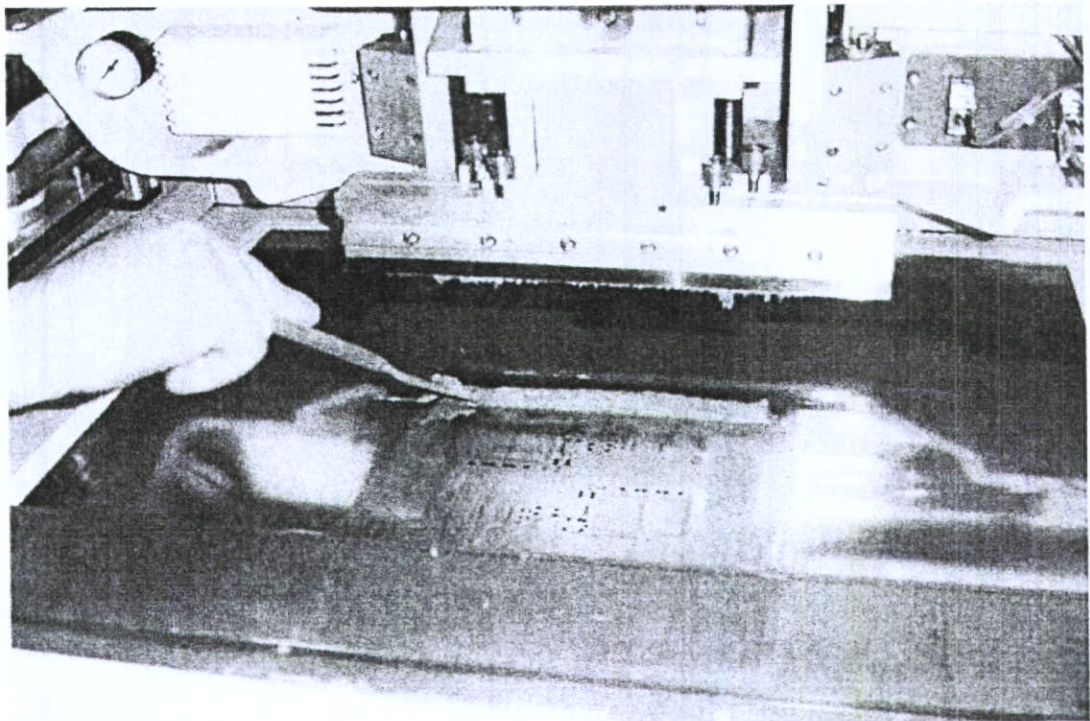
Aplicación de la soldadura en pasta antes de la impresión.
